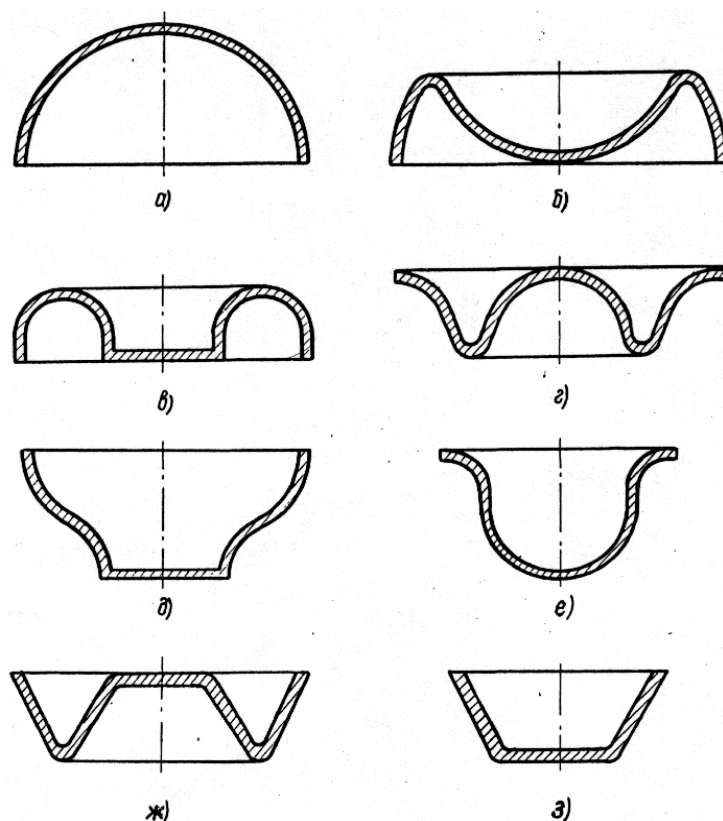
Типовые формы деталей, формообразуемых процессом фрикционно-реверсивной вытяжки эластичной средой по жесткой матрице: *a* – сферические и сферообразные детали-оболочки; *б* – детали знакопеременной кривизны, в том числе полуфабрикаты для получения сферообразных оболочковых деталей с равномерной толщиной стенки; *в* – горообразные детали или полуфабрикаты для получения конусообразных оболочек со знакопеременной образующей (*д*); *г, ж* – сложноконтурные полуфабрикаты для получения глубоких сферообразных (*е*) и конических (*з*) деталей из плоской заготовки
